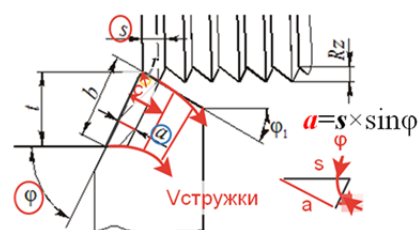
Основные параметры геометрии токарного резца и режима резания на виде сверху при несвободном косоугольном резании
